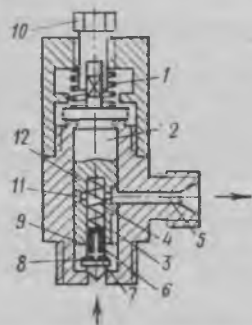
Сдвоенный нагнетательный клапан для двойной подачи топлива: 1 — пружина; 2 — подвижной элемент; 3 — продольный паз; 4 — регулирующая кромка; 5 — канал для нагнетания топлива в форсунку; 6 — нагнетательный клапан; 7 — радиальные отверстия; 8 — посадочный конус; 9 — запорное седло; 10 — регулятор поворота подвижного элемента; 11 — кольцевая канавка для прохода топлива; 12 — радиальные сверления в канавке
